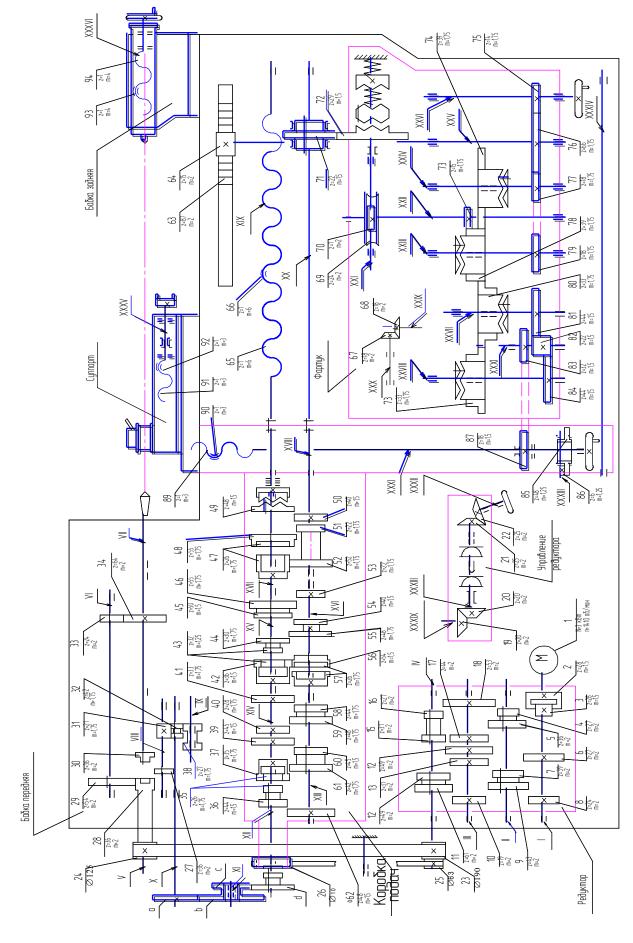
Кинематическая схема. Редуктор исп. 2
